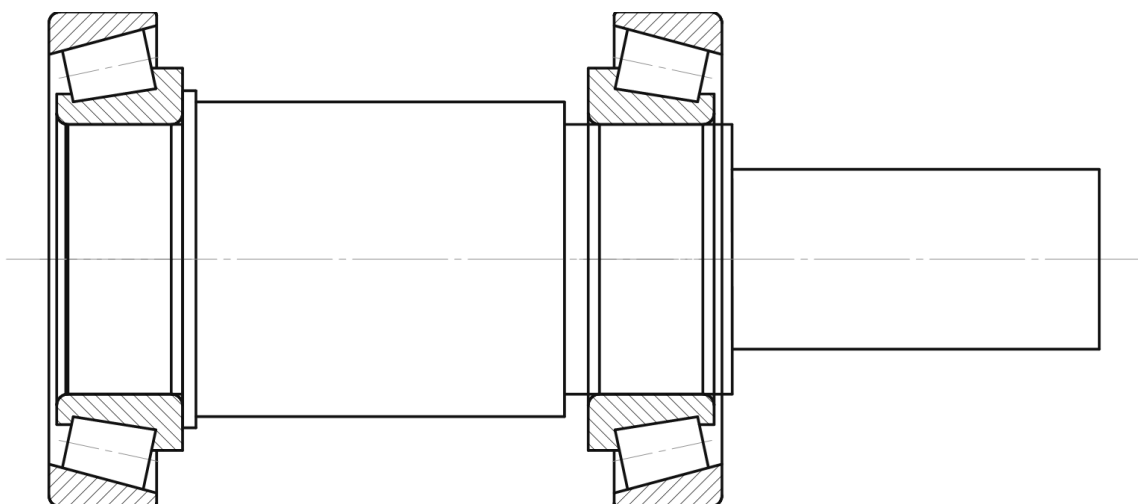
Ескіз підшипникового вузла колеса черв'яка
